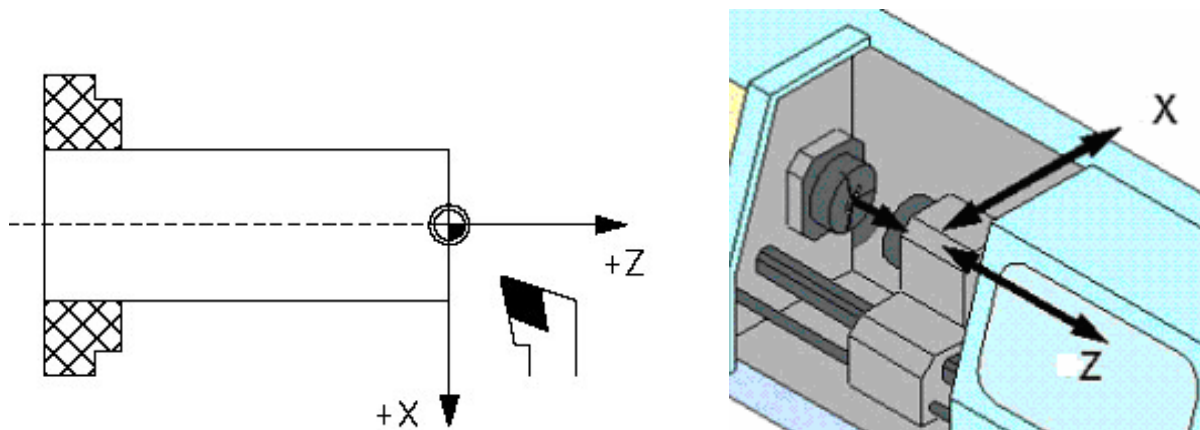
Схема рабочей зоны станка и направления перемещений инструментов
